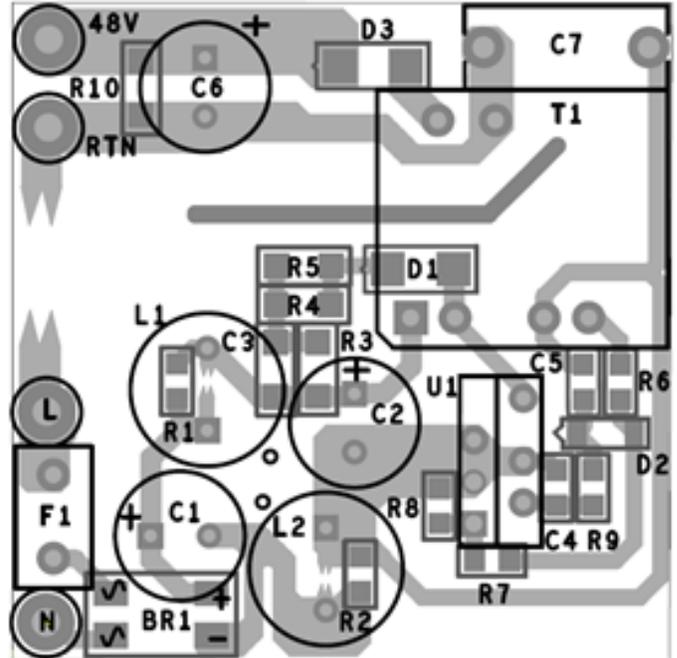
eSIP 패키지를 사용하는 PCB 레이아웃 예
